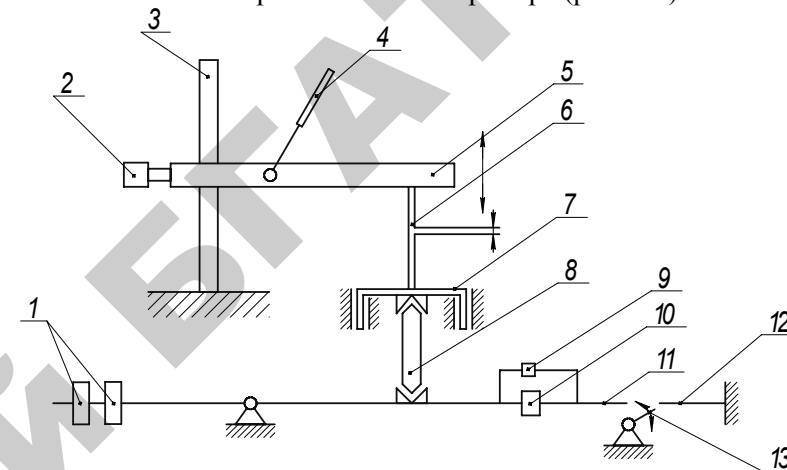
Схема проверки упругости поршневого кольца на приспособлении МК-ПР-562:
